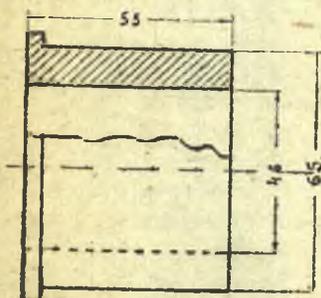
Втулка для заготовки  $\varnothing 45$  мм для 1-й обточке до  $\varnothing 31,9$  мм по длине 1800 мм
